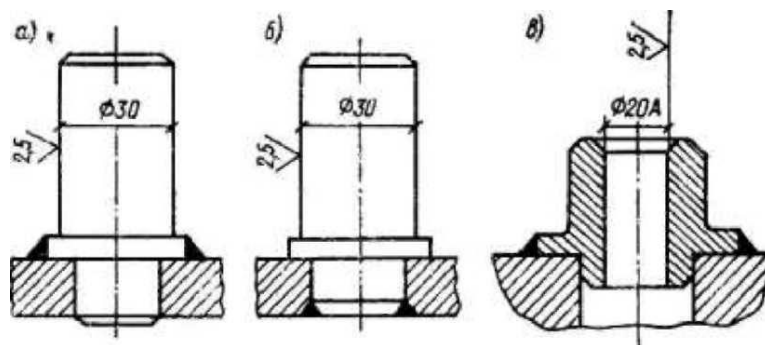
Схема установки привариваемых чисто обработанных фиксаторов:
